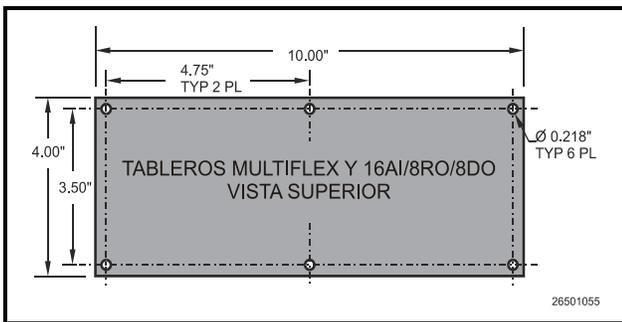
Dimensiones de Montaje de 16AI/8RO/8DO
